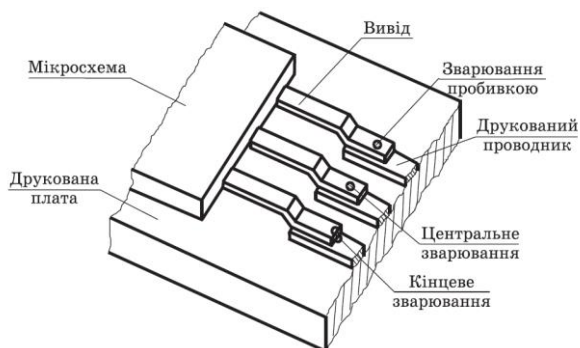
Форма з'єднання при лазерному зварюванні
